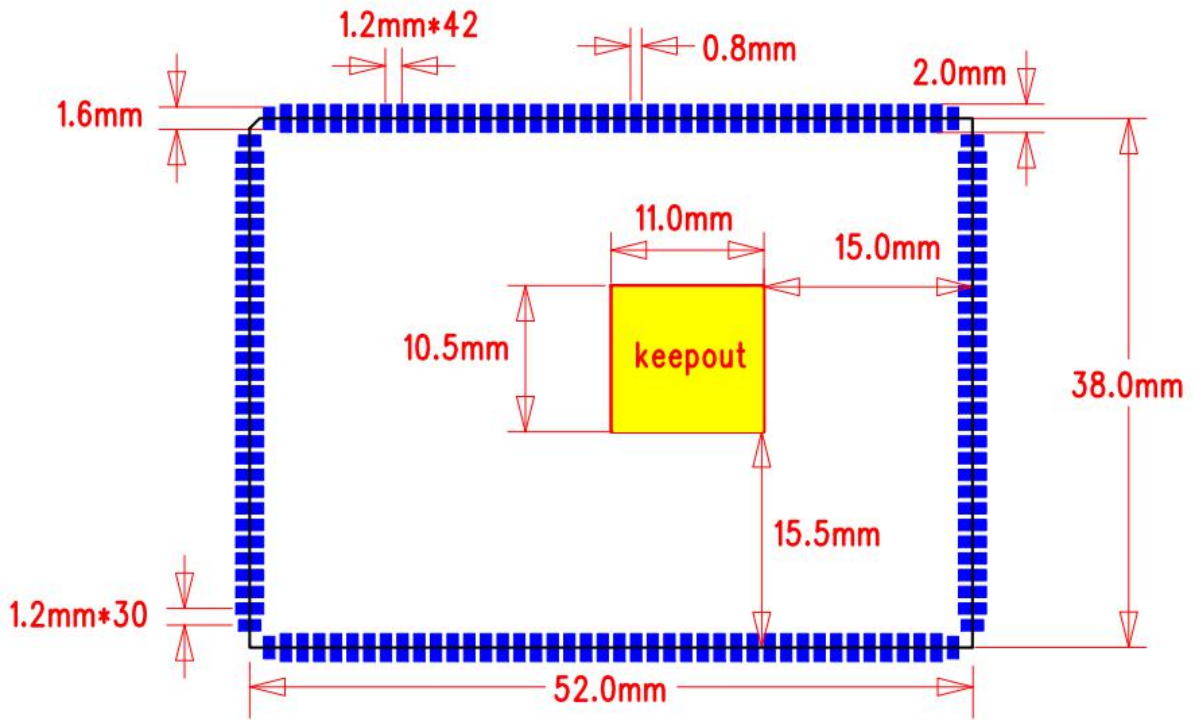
推荐的 PCB 封装焊盘尺寸(单位, mm)
